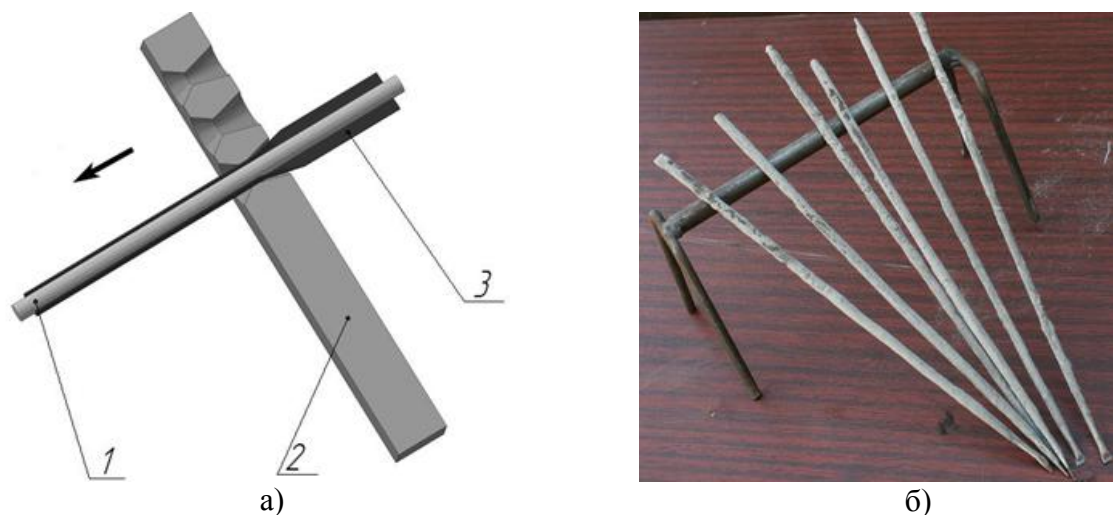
Схема протяжки трубки (а): 1 – стержень, 2 – фильера, 3 – пластина; экспериментальные образцы порошкового электрода (б)
